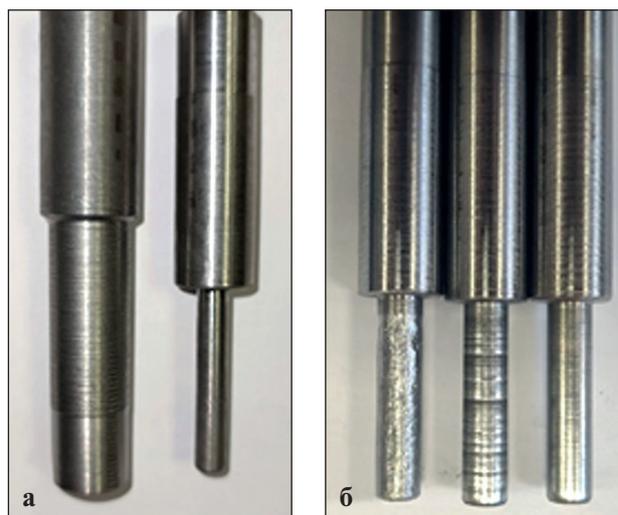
Нестандартные образцы для исследования влияния шероховатости поверхности металла на адгезионную прочность при взаимодействии композиционного материала со сталью: а – внешний вид образцов; б – образцы с разной шероховатостью стержней
